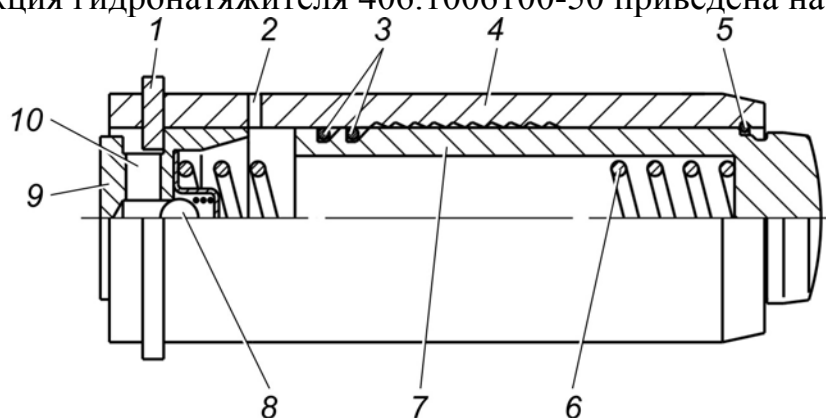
Гидронатяжитель 406.1006100-50: 1 – кольцо; 2 – отверстие для перепуска масла; 3 – запорные кольца; 4 – корпус; 5 – стопорное кольцо; 6 – пружина; 7 – плунжер; 8 – шариковый клапан; 9 – дроссель с клапаном в сборе; 10 – отверстие для подвода масла
